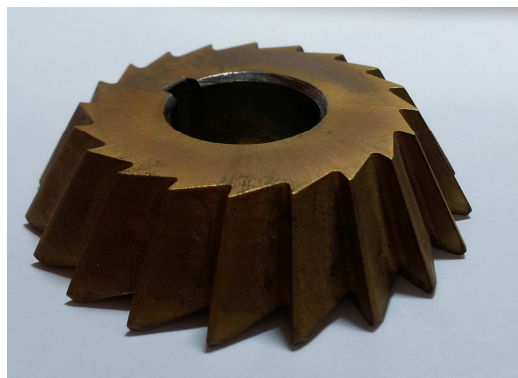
Общий вид фрезы с углом наклона режущих кромок зубьев 60°
